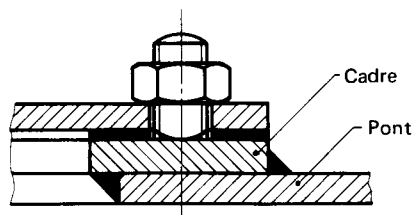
Soudure intérieure au-dessous du cadre
